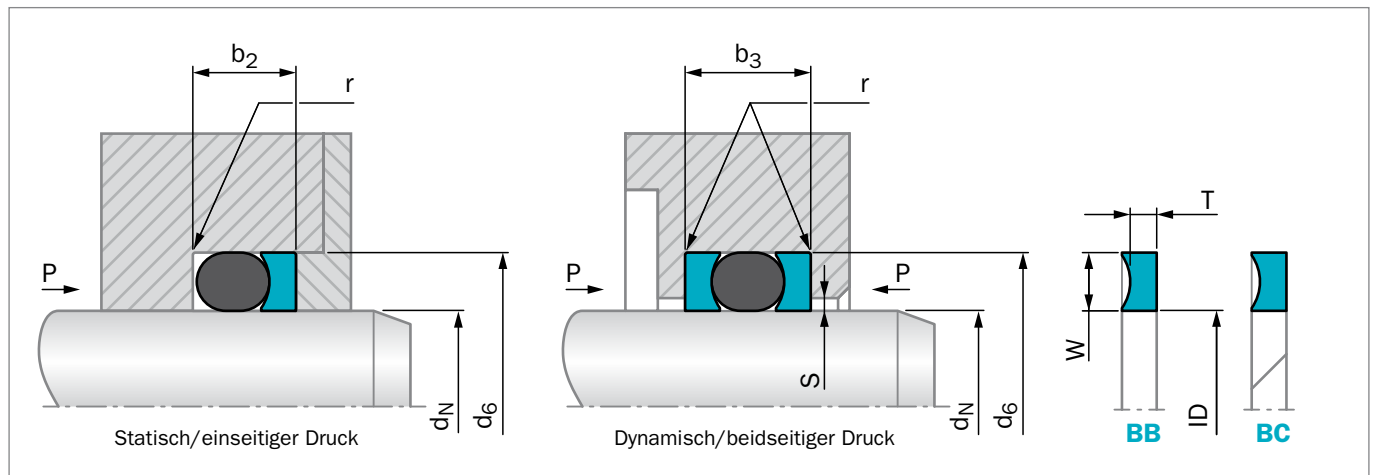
Einbauzeichnung innendichtend, konkave Stützring-Typen
